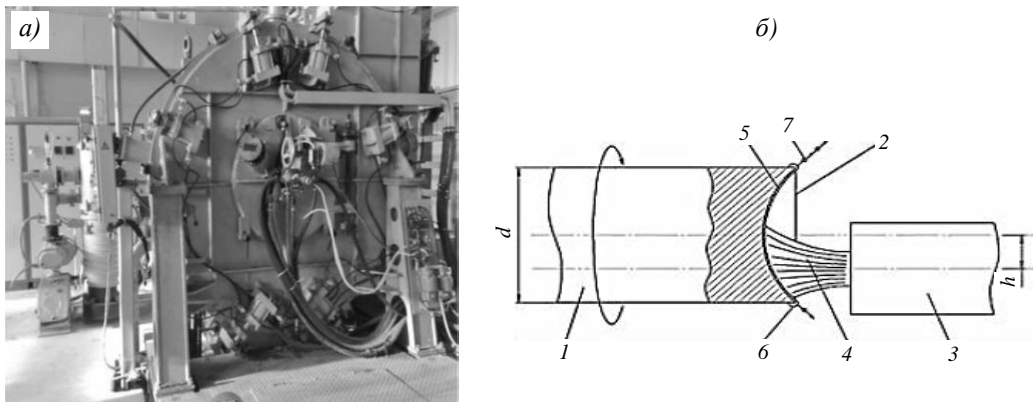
Установка типа УЦР плазменной плавки с центробежным распылением литой вращающейся заготовки (метод PREP) для получения гранул жаропрочных никелевых сплавов (*а*) и схема формирования гранул (*б*): *1* – литая заготовка с диаметром *d*; *2* – торец заготовки; *3* – плазматрон с эксцентриситетом *h*; *4* – поток плазмы; *5* – пленка расплава; *6* – тороидный венец из расплавленного металла; *7* – капли жидкого металла (гранулы)
